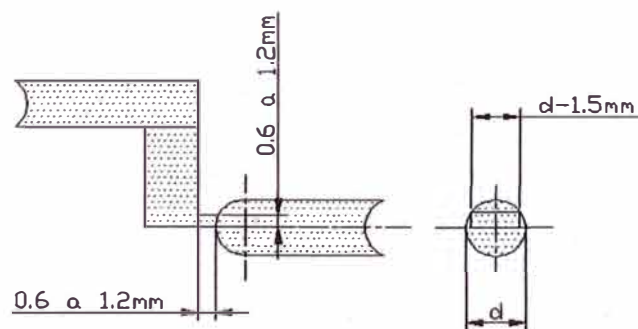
Dimensionado de un canal de estrangulamiento (Entrada)
